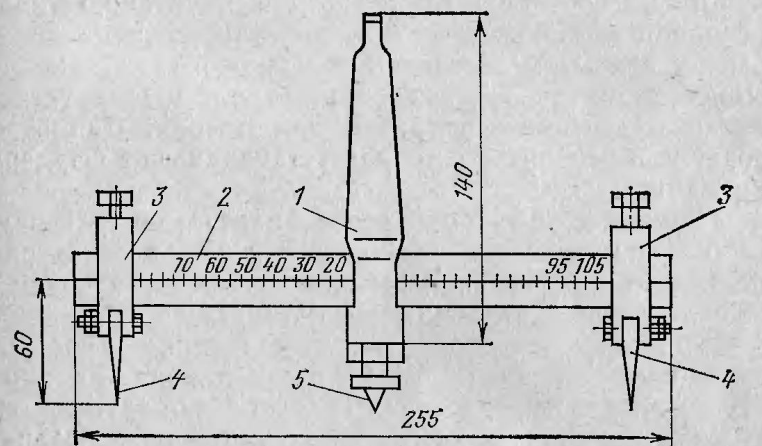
Приспособление для вырезки прокладок на сверлильном станке.
